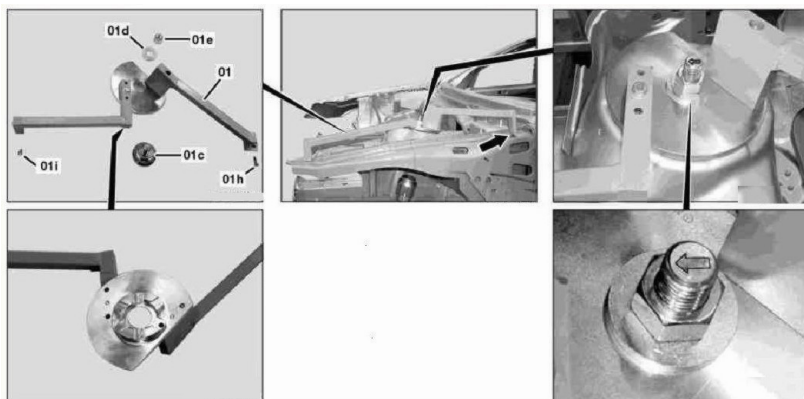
Использование приспособления для ремонта (или замены) переднего верхнего правого лонжерона (балки): 01 – приспособление для проверки и сварки; 01с – винт центрирующий; 01d – подкладная шайба; 01 e – гайка центрирующего винта; 01 h – винт М6; 01 i – винт М6
